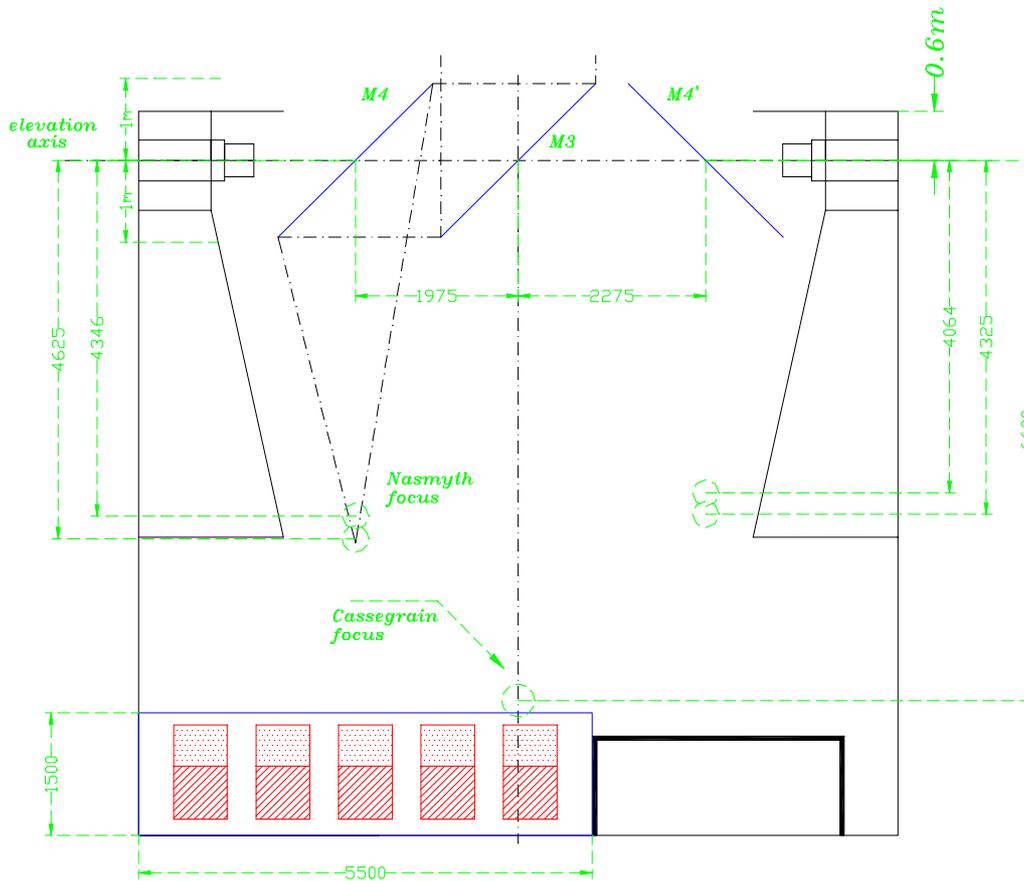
Geometría general del interior de la cabina de receptores. Vista en planta.
